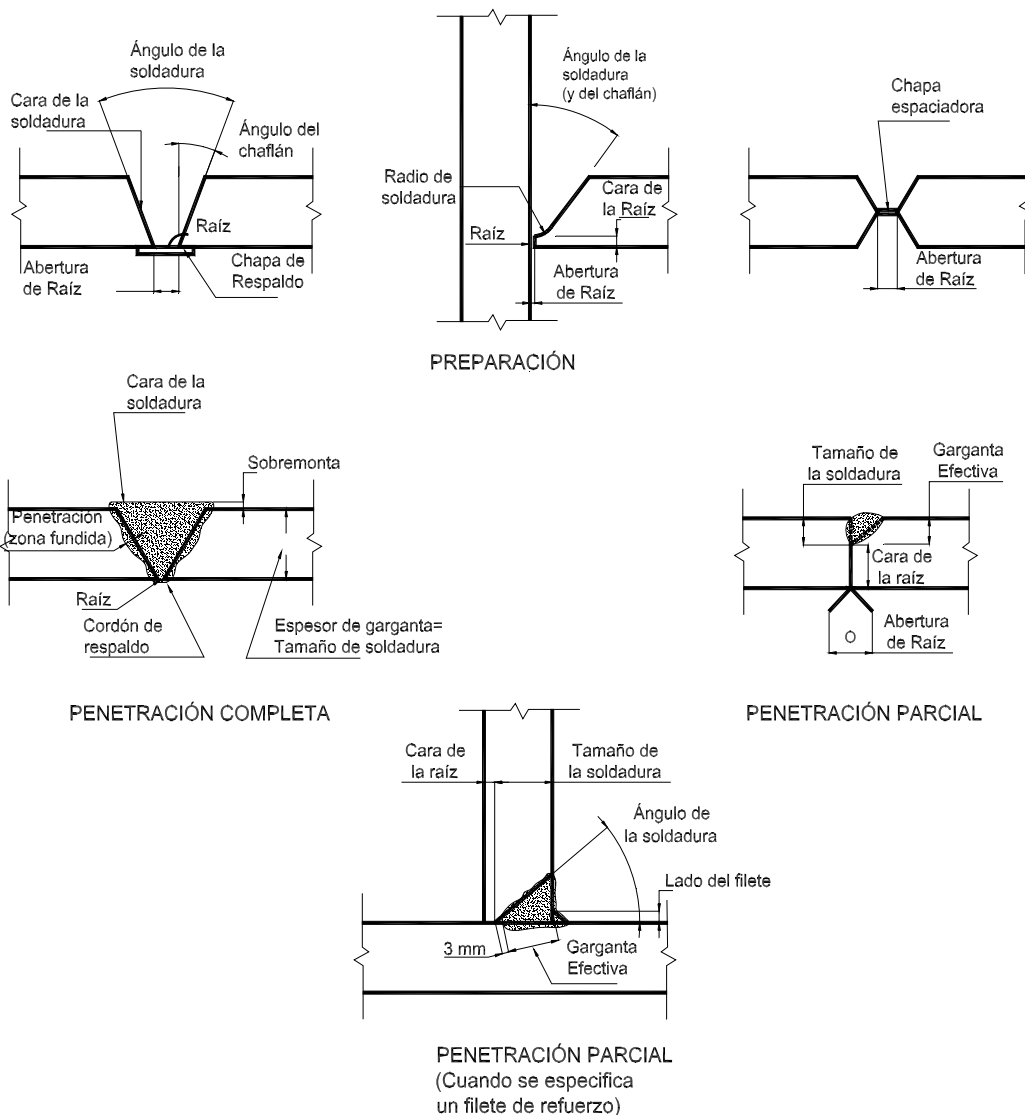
Nomenclatura de soldaduras a tope.
